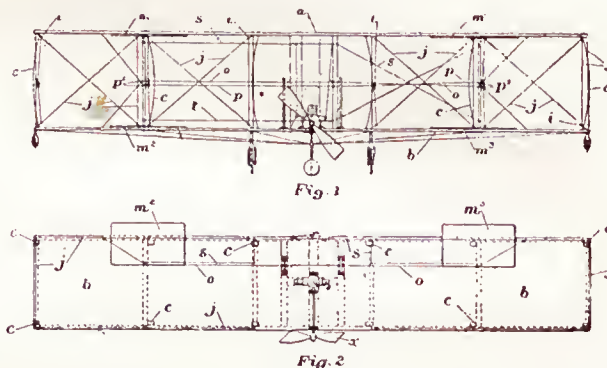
e 19. - Aeroplano Chappel. Elevazione e pianta.
